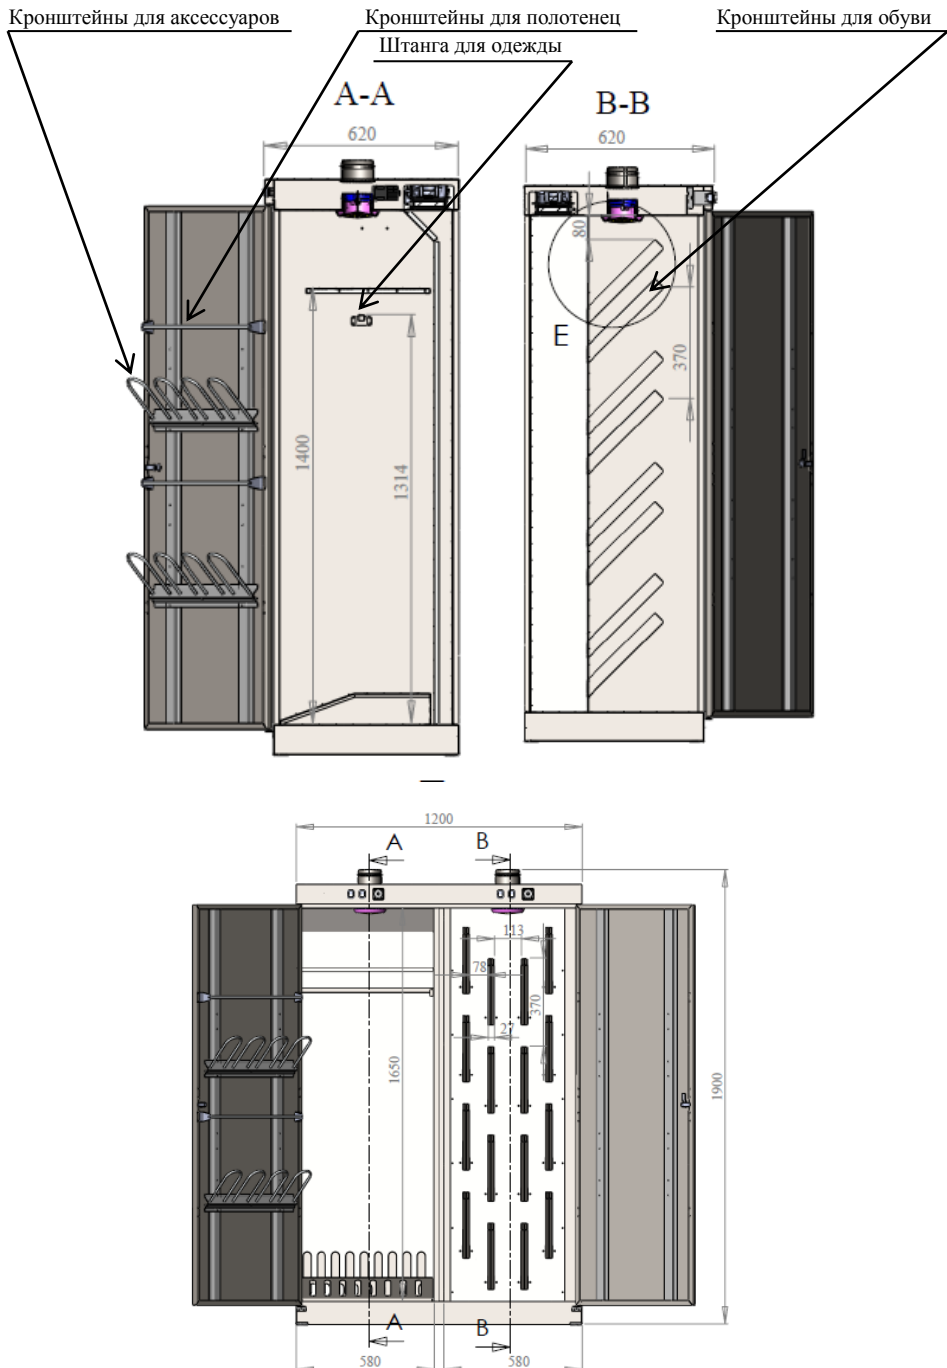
Внешний вид и габаритные размеры Шкафа Сушильного ШС – 4 - 8.
